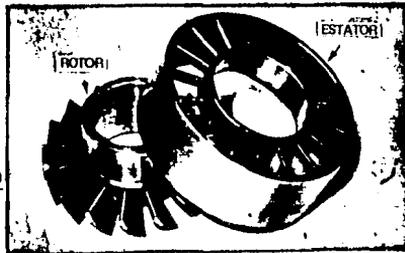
B. ENSAMBLE DE ROTOR Y ESTATOR
